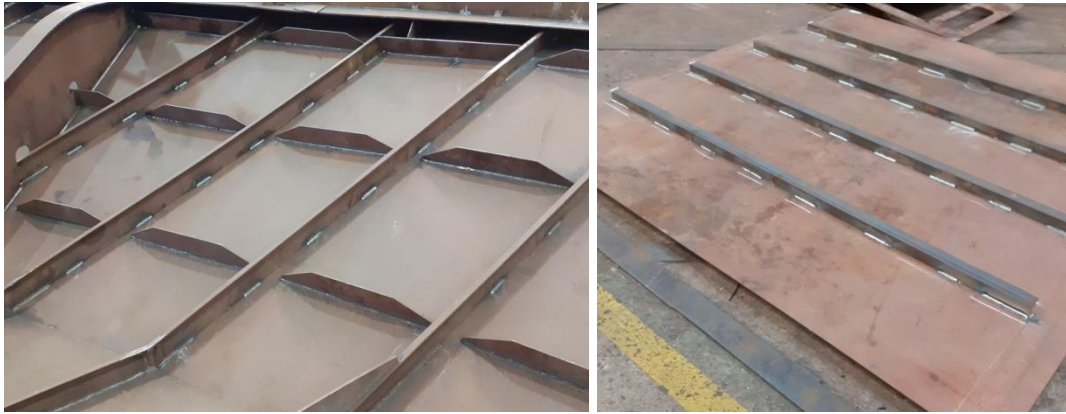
Soldaduras intermitentes (fonte: West-sea)
